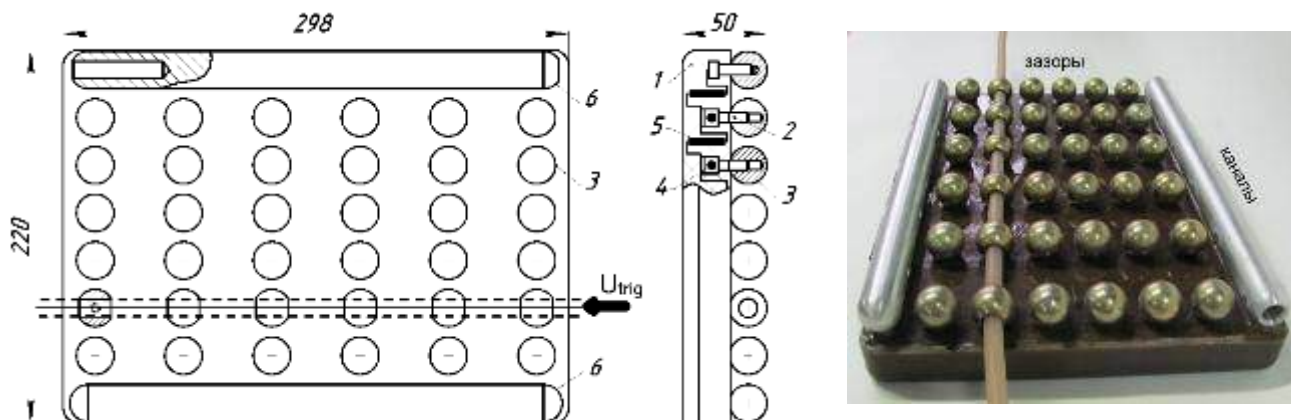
Первый вариант разрядника: 1 – корпус разрядника; 2 – детали для крепления электродов; 3 – электроды разрядника; 4 – шнуры из проводящей резины; 5 – резистивный делитель напряжения; 6 – высоковольтный и низковольтный концевые электроды
